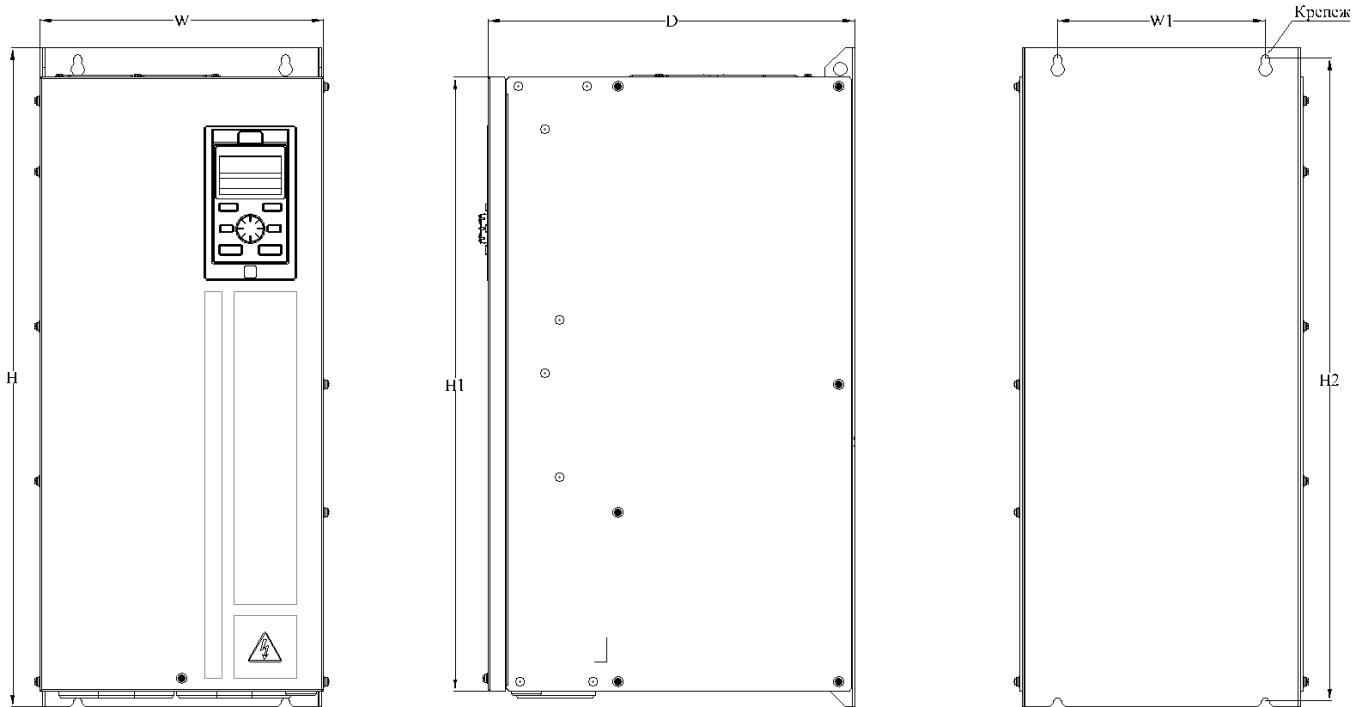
Чертеж преобразователя частоты типоразмер 6
